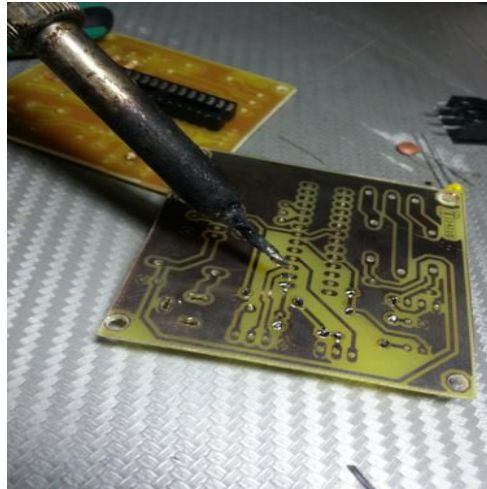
Soldado de los componentes electrónicos en la placa
